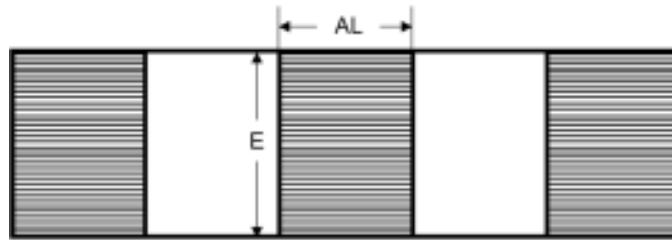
Sección transversal de la columna del núcleo trifásico
